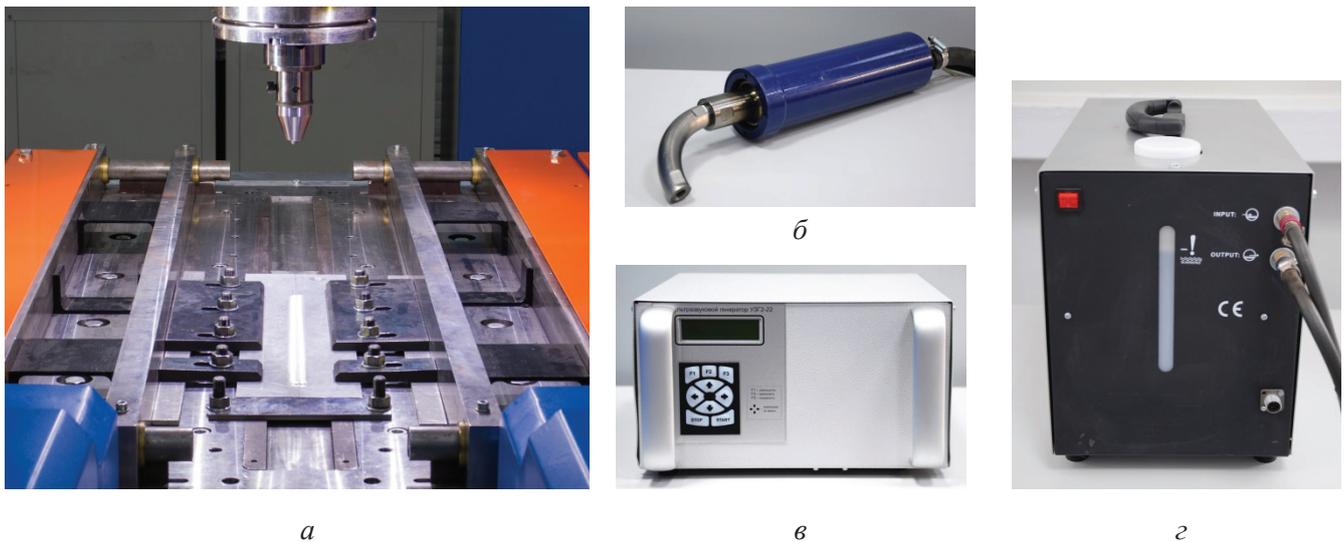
Экспериментальный стенд для сварки трением с перемешиванием с ультразвуковым воздействием: рабочий стол оборудования (а); магнитоистриктор с сонодами первой и второй ступени (б); генератор ультразвуковых колебаний (в); охладитель (г)
